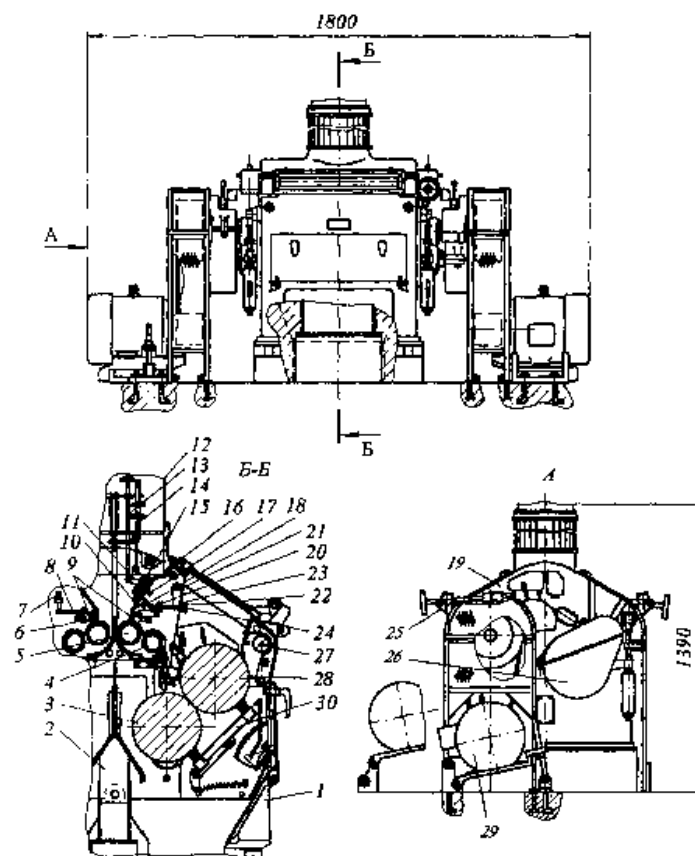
Двохсекційний вальцевий верстат 3М2: станина 7; вальці 3 і 28; розподільний 4 і живильний 5 вальці; аспираційний пристрій 2; важелі 6, 11, 15, 23; гвинти 7, 17, 24; планка 8; секторна заслінка 9; пружини 10, 22; живильна труба 12; датчики 13 і 14; механізм грубого привалу 19; механізм 25 регулювання і вирівнювання рухомого вальця; міжвальцьову передачу 26; ексцентриковий вал 27 і електродвигун 29.
